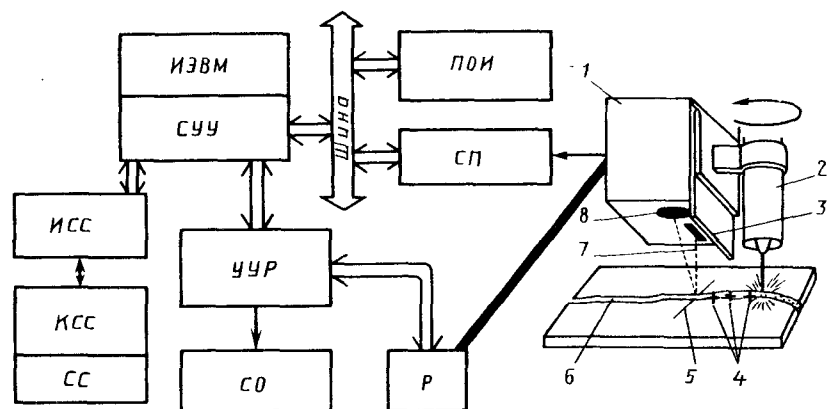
Схема системы дуговой сварки роботом с СТЗ:
